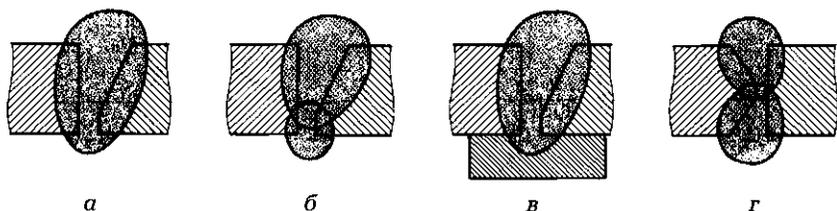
Стыковое сварное соединение со скосом одной кромки (а—в) и двумя симметричными скосами одной кромки (г)
